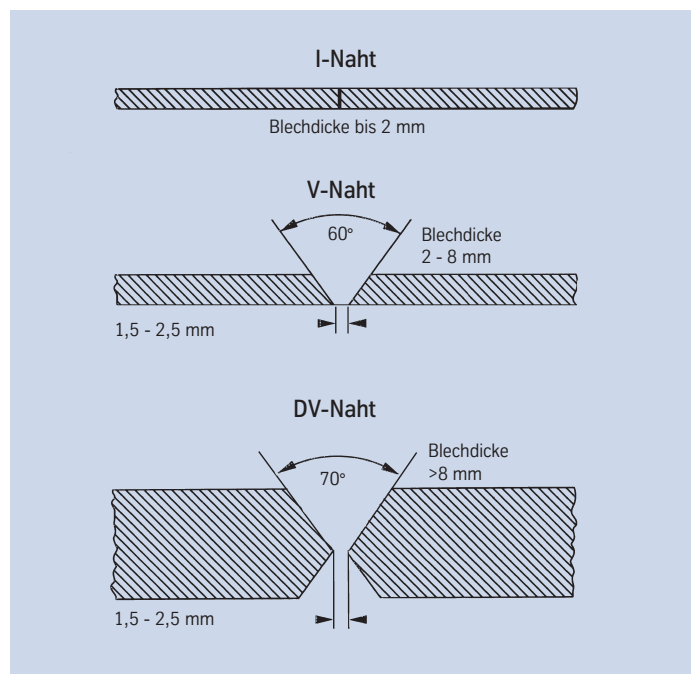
Nahtvorbereitung für das WIG-Schweißen von Pernifer 36.
